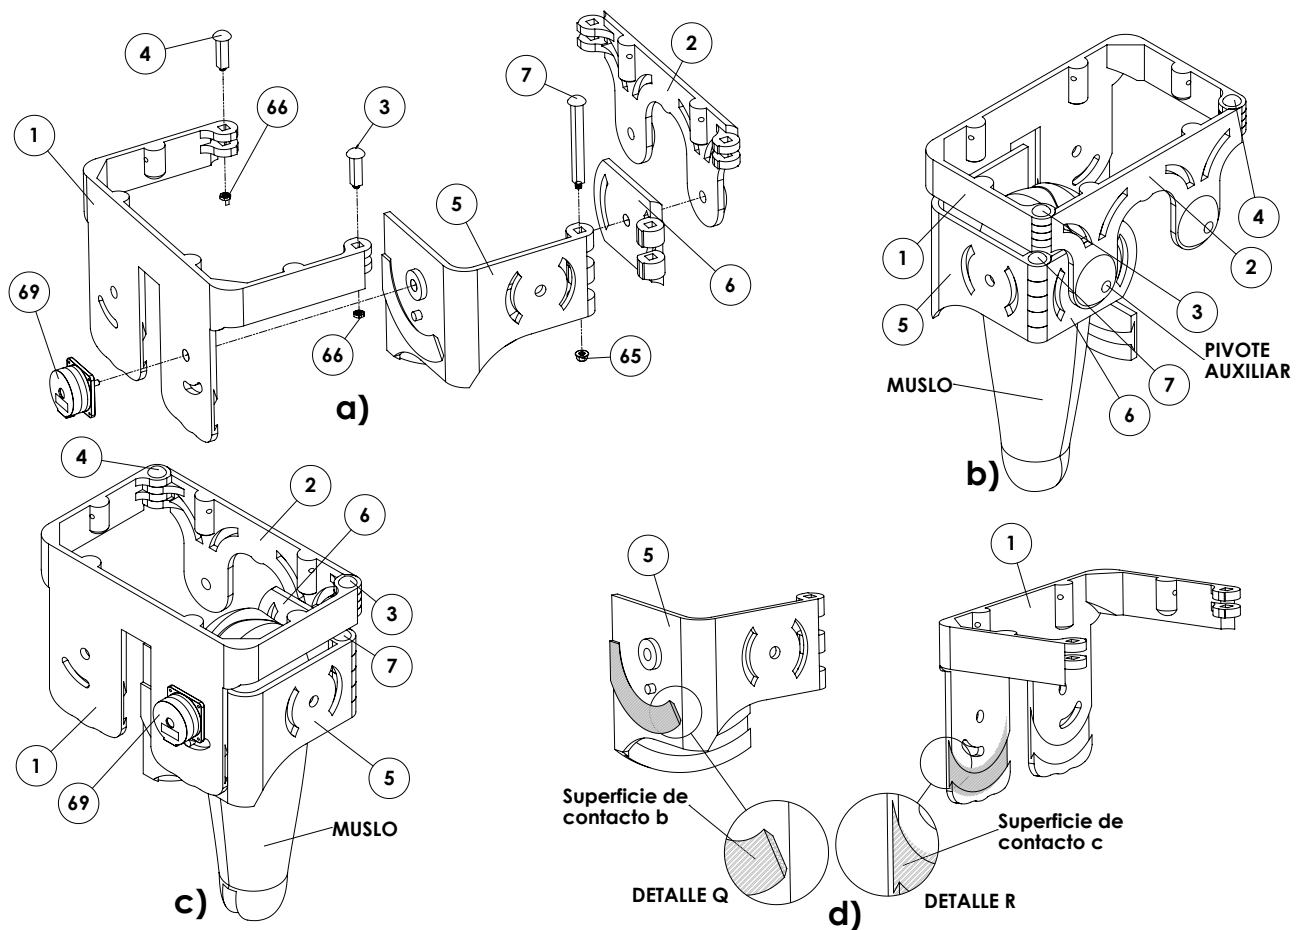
Elementos del exoesqueleto para movimiento de cadera en plano frontal: a) Explosionado de elementos. b) Componentes de estructura colocadas en muslo, vista isométrica frontal. c) Componentes de estructura colocadas en muslo vista trimétrica posterior y ubicación de actuador. d) Guía de *cola de milano* empleada.
